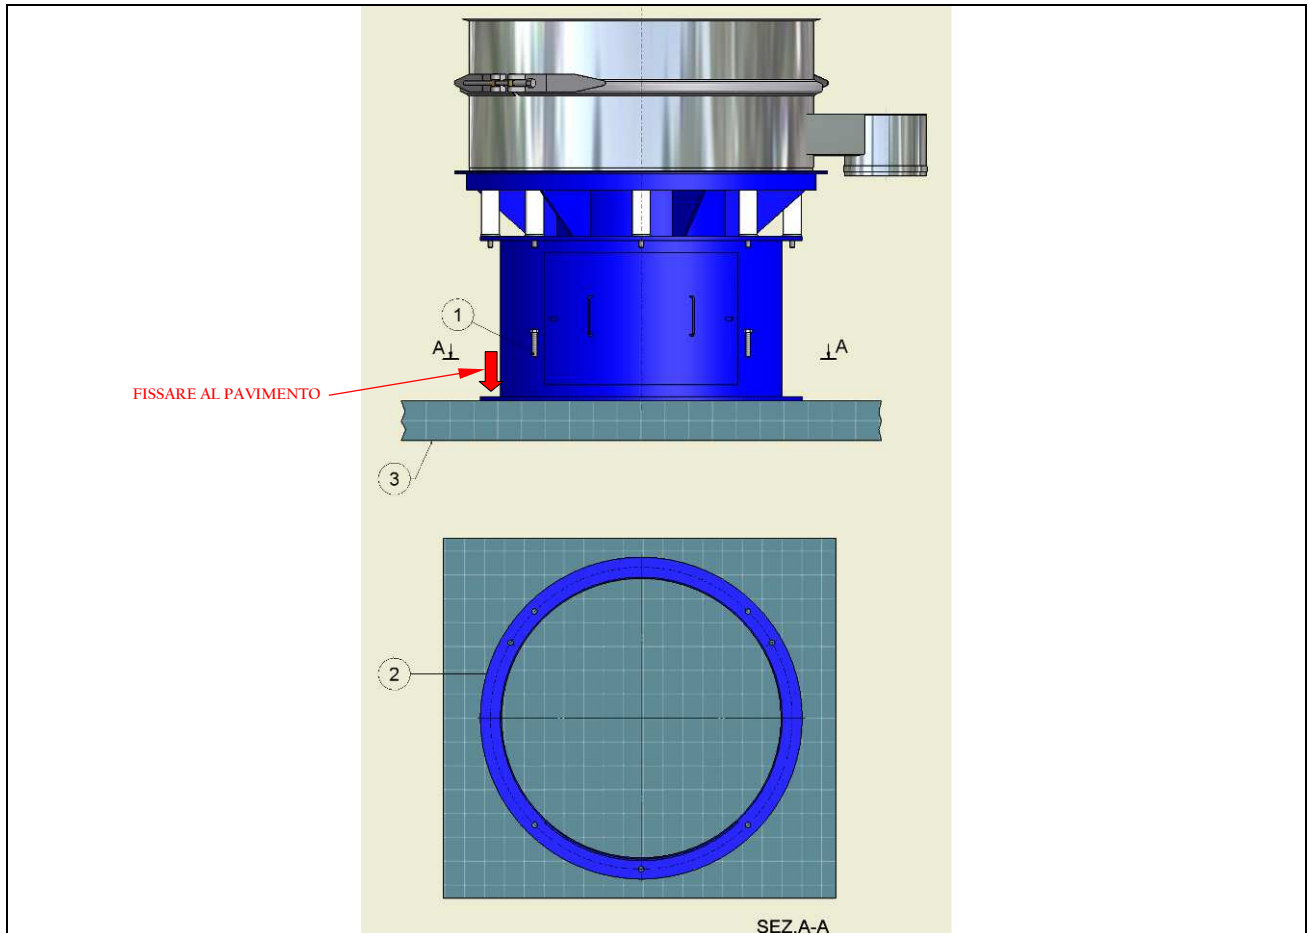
Fissaggio del Sistema su pavimentazione di cemento
